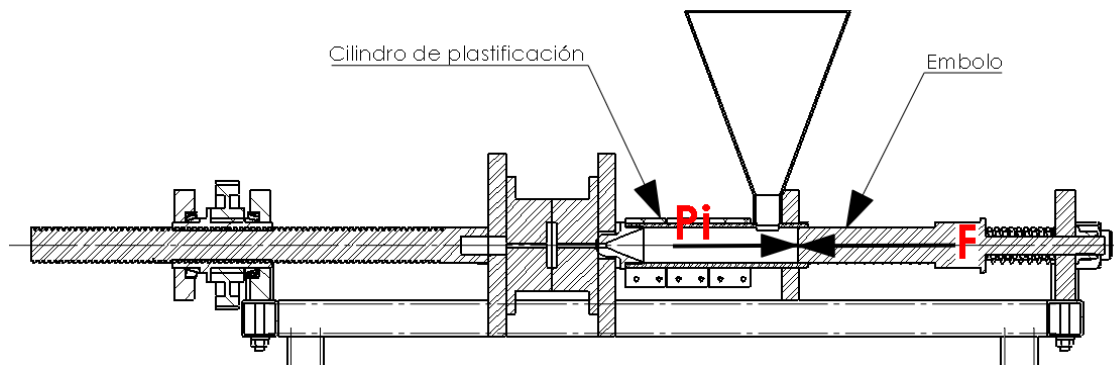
Vista lateral de la sección de plastificación, esfuerzos en el eje de inyección.
